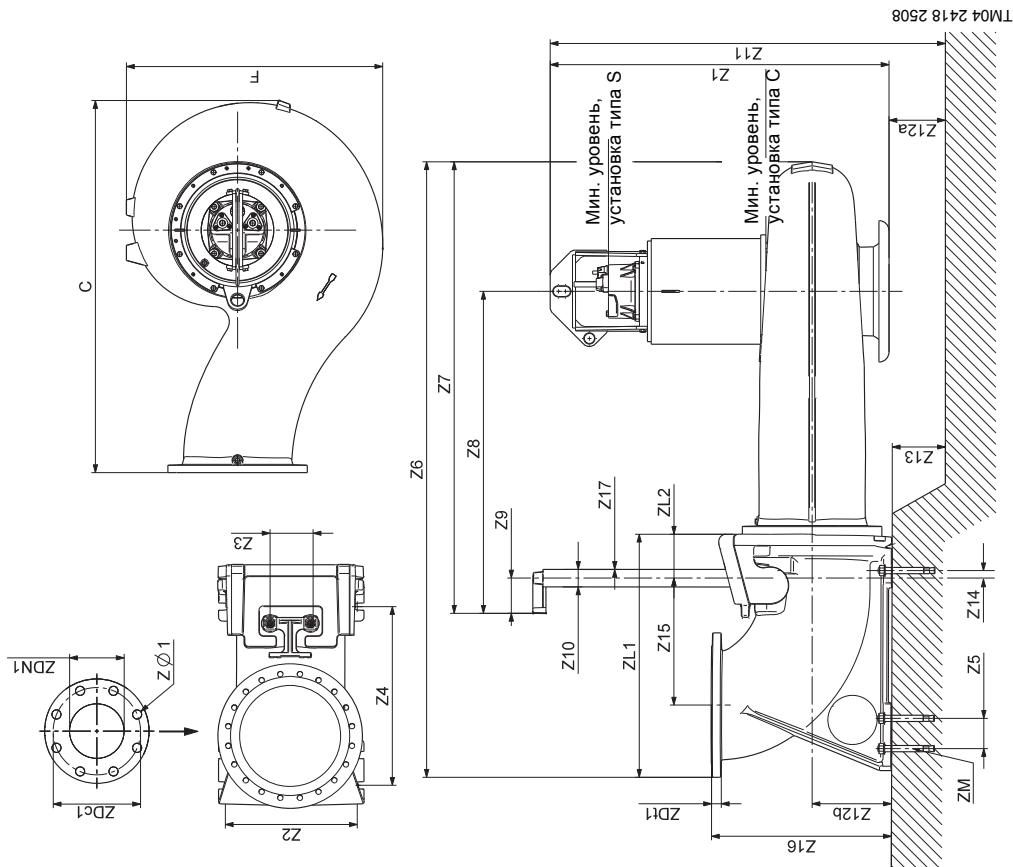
Габаритные размеры, установка на автоматической трубной муфте
